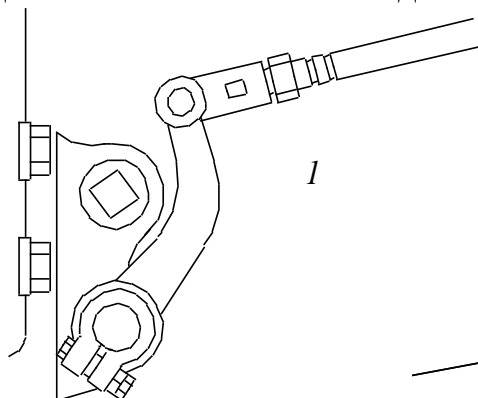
Резьбовое отверстие смазки подшипника отводки сцепления: 1 – пробка
